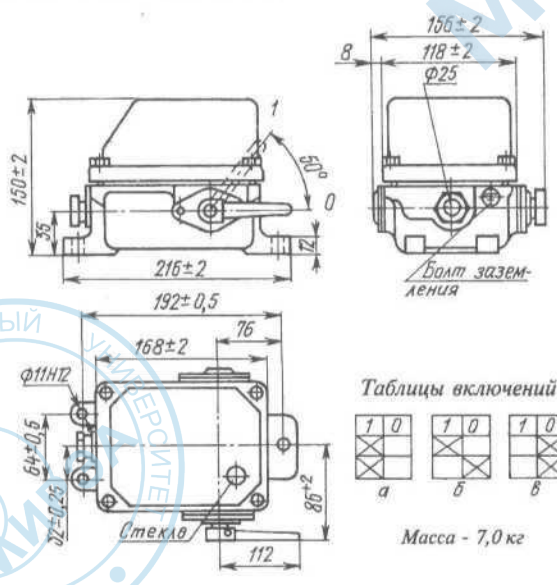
Габаритные, установочные размеры и масса выключателя типа ВУ-742
